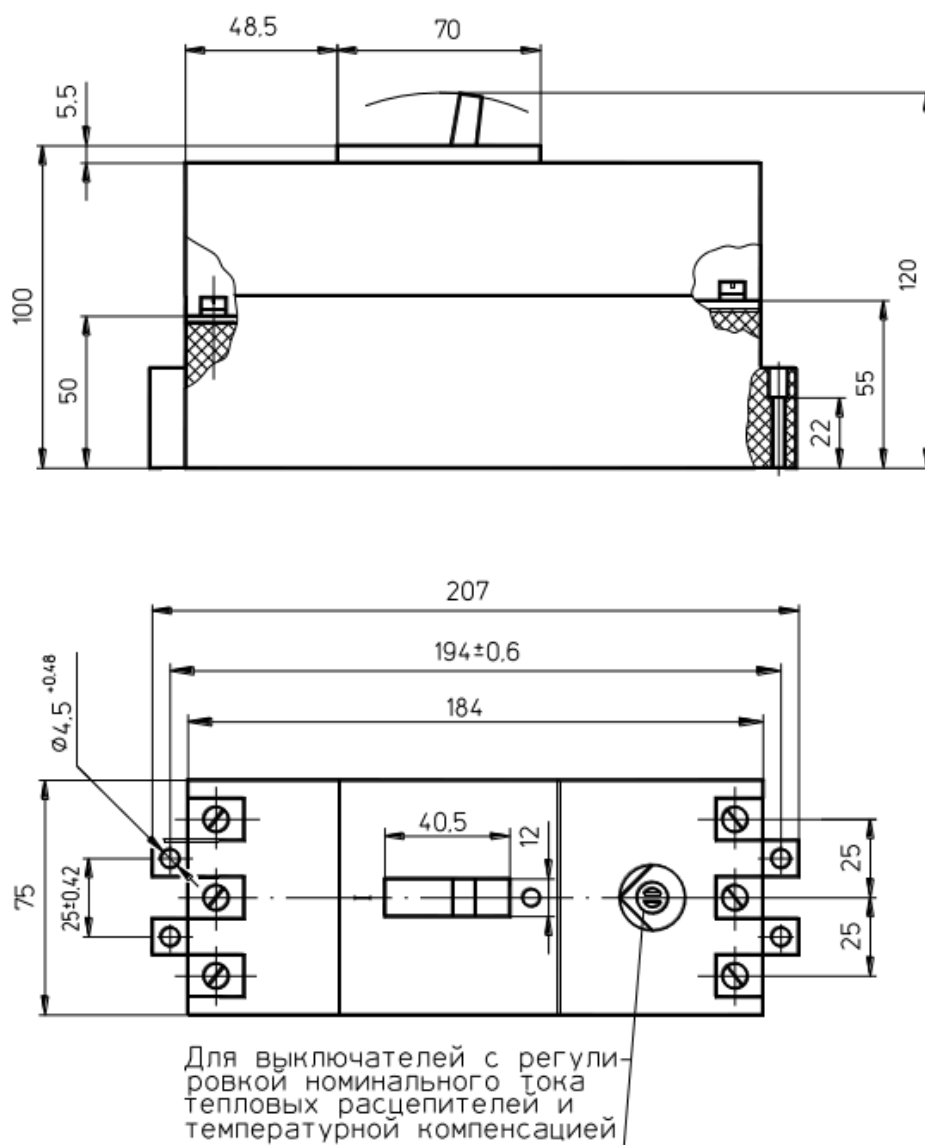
Габаритные размеры выключателя АЕ 2056
